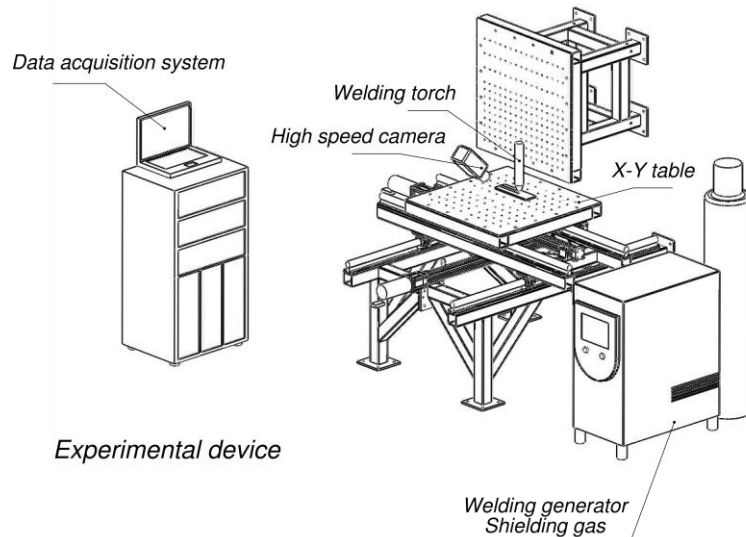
Vue générale de la plateforme expérimentale modulaire de soudage
